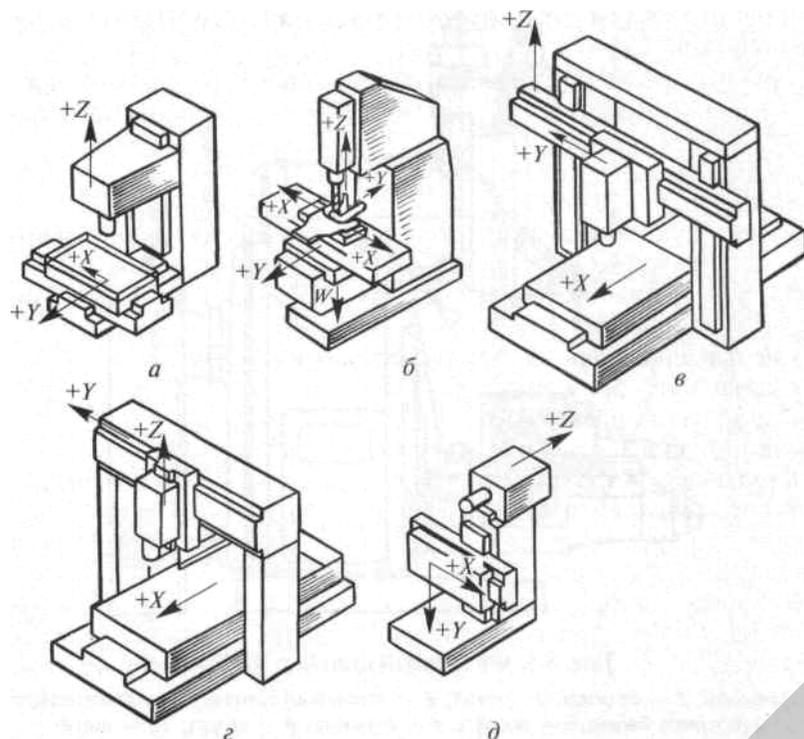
Компонки фрезерных станков с ЧПУ с обозначением осей координат X, Y, Z и W:
